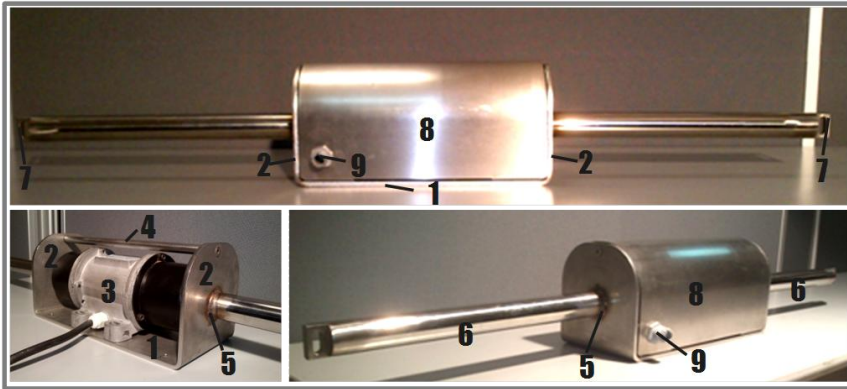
Detalle de los componentes estructurales del prototipo II de barra vibratoria en la primera fase. Superior, vista en alzado lateral del prototipo II, fabricado íntegramente en acero inoxidable; inferior, vistas en perspectiva del prototipo con el motor a la vista (izquierda) y con el recubrimiento extraíble fijado (derecha).
